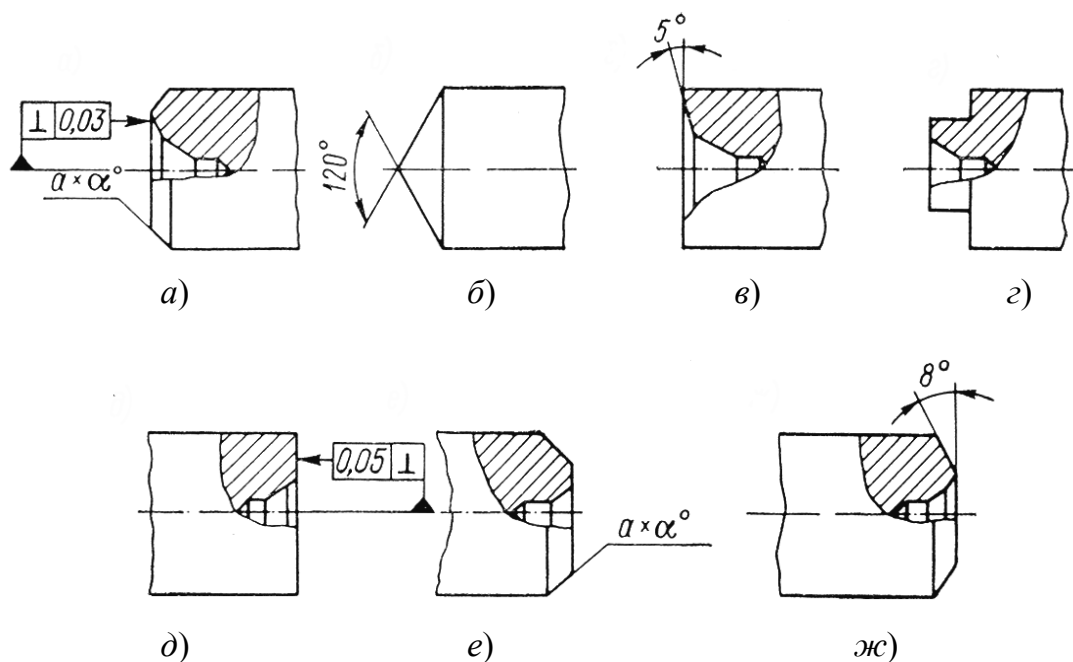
Эскизы торцов заготовок концевых инструментов
